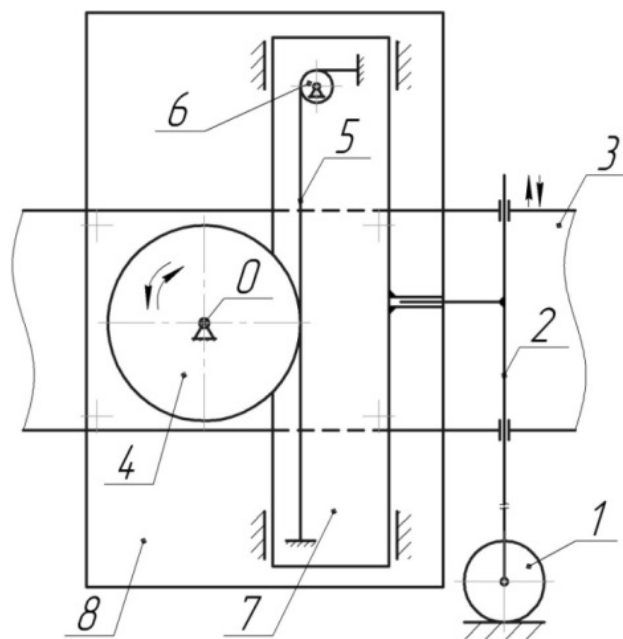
Структурна схема датчика-перетворювача для досліджень кутових переміщень рами плуга: 1 – колесо-копір; 2 – стійка колеса; 3 – рама плуга; 4 – шків-перетворювач; 5 – стальна струна; 6 – натяжний пристрій; 7 – напрямна платформа; 8 – базова платформа.
